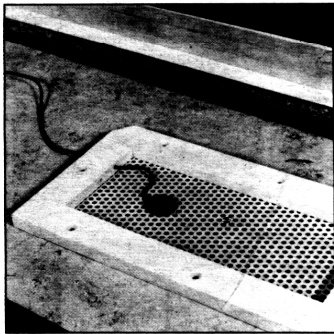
Den Lötspunkt bringt man am besten vor dem Pulver-Einbrennvorgang auf das Lochblech. Nach dem Kabelanschluß sollte man hier eine Isolierkappe anbringen.
